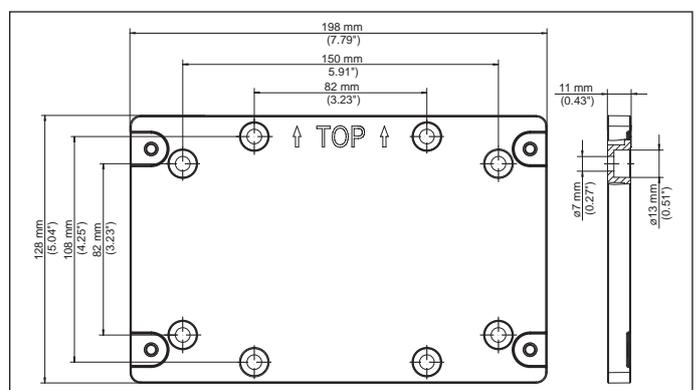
Dimensioni piastra di montaggio VEGAMET 861, 862
